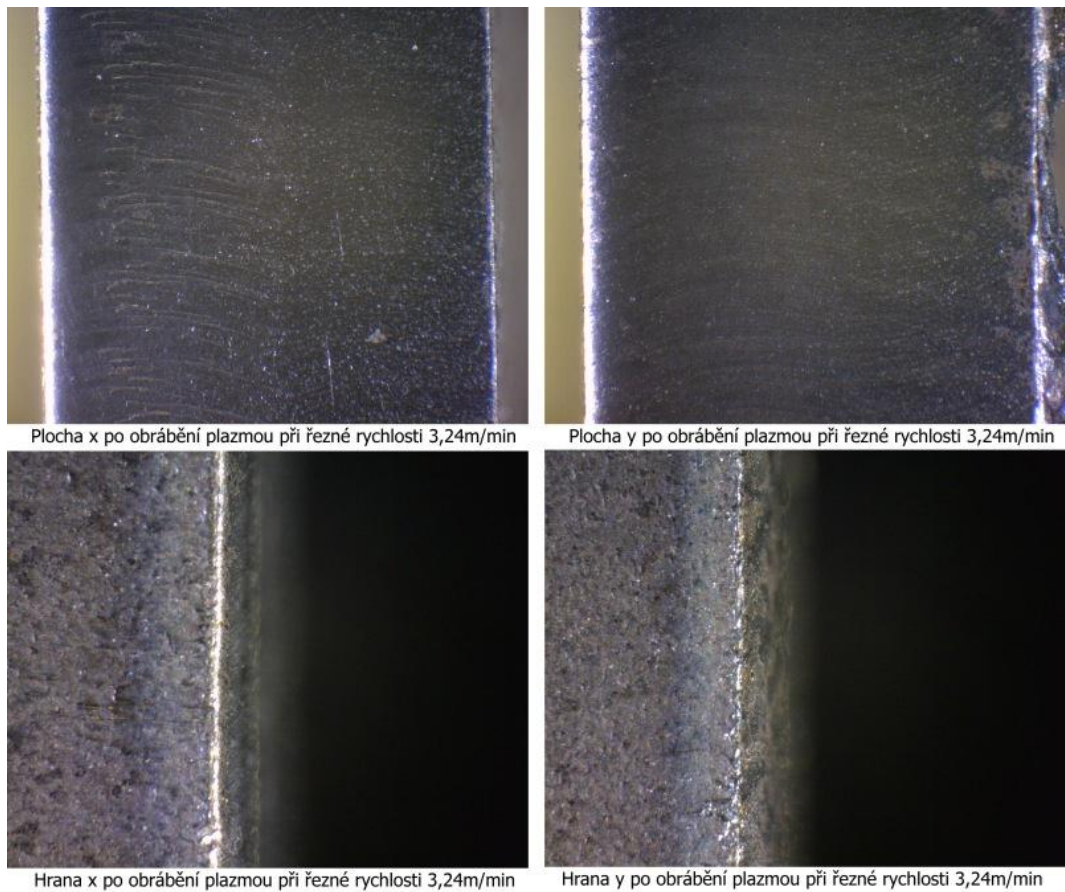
Snímky z mikroskopu vzorku 1 obráběného plazmou - materiál 11 375
